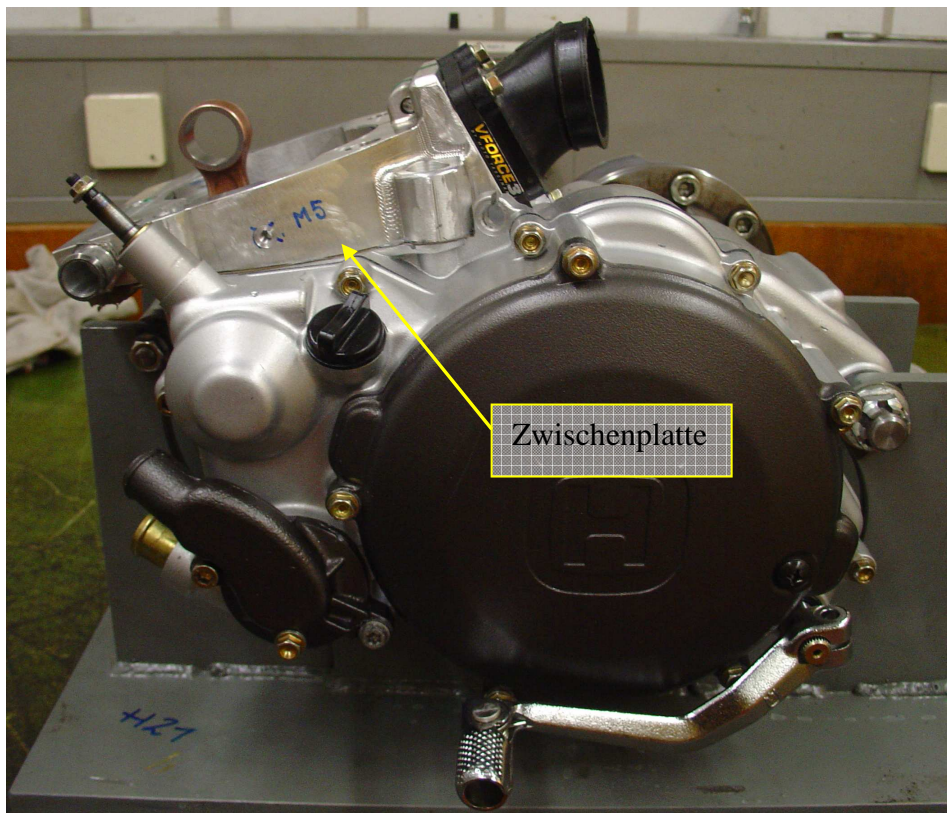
Motorgehäuse mit Zwischenplatte
